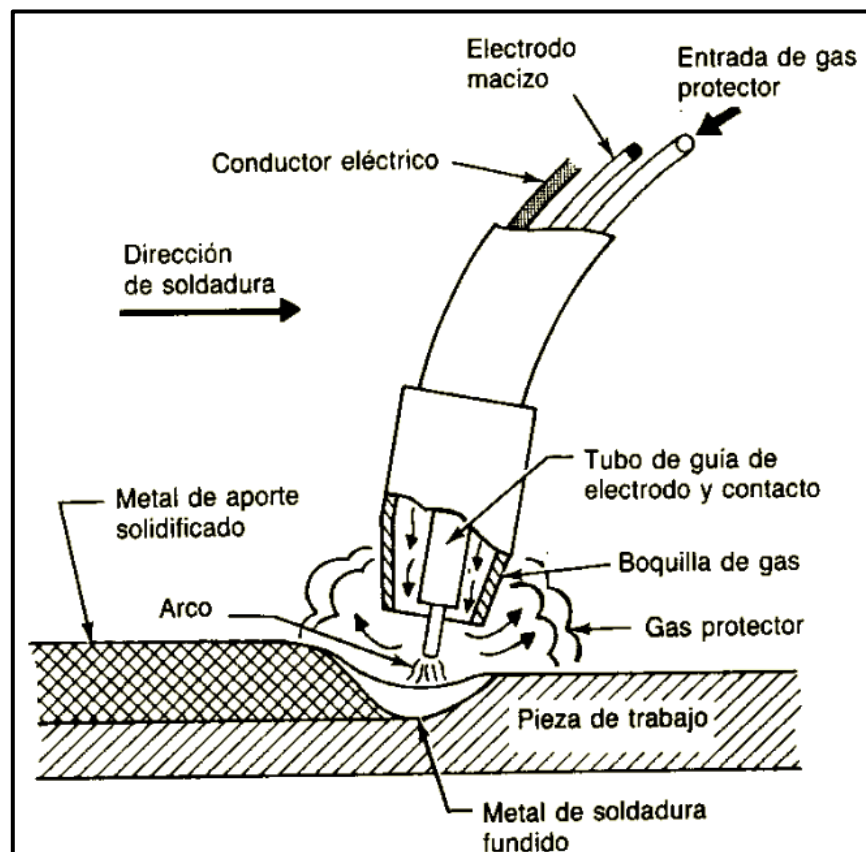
Representación del proceso de soldeo por GMAW. Fuente: ILMO
